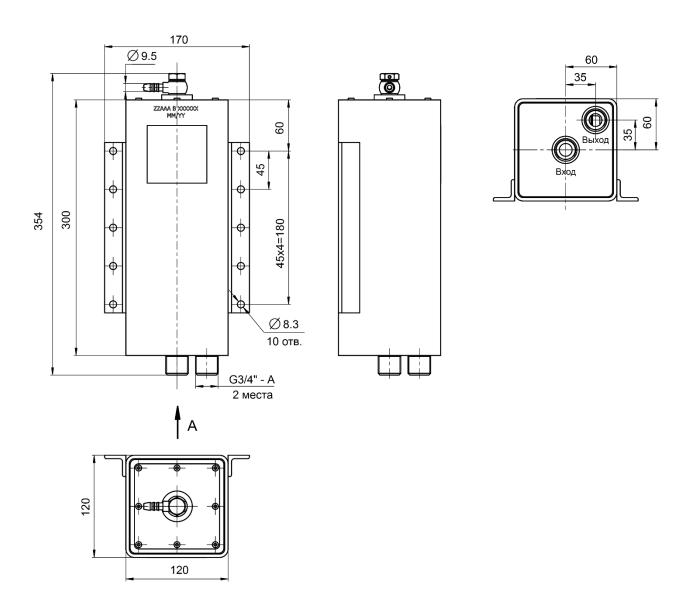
Габаритные размеры деаэратора <u>DFM DA 600</u>
